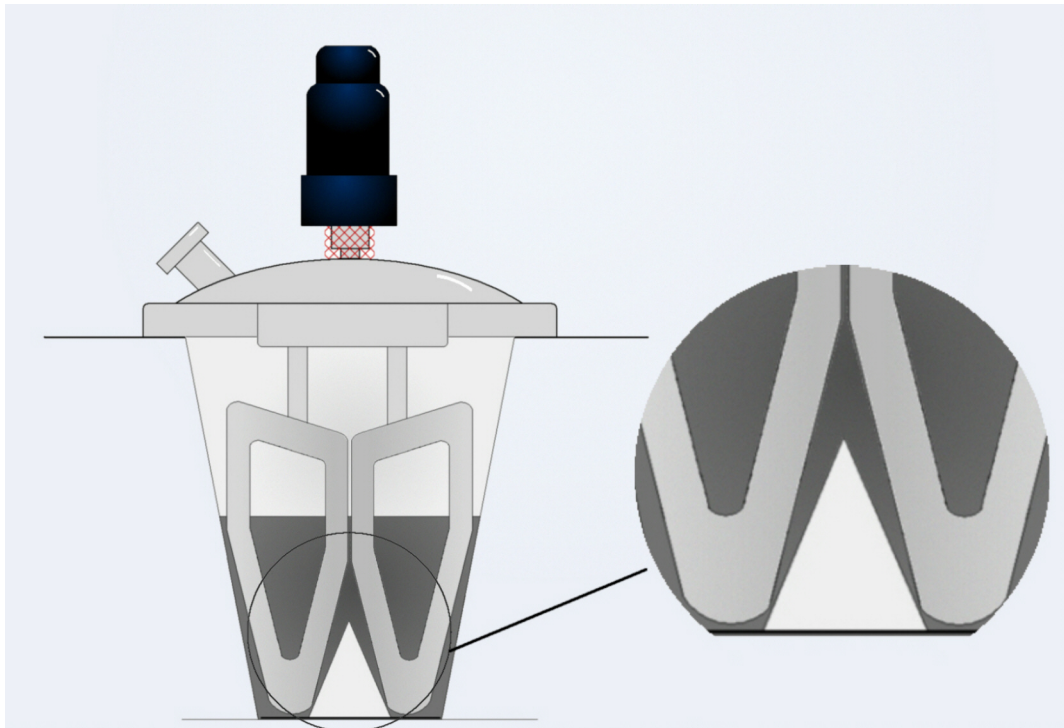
Esquema de una máquina de moldeo por inyección a baja presión
